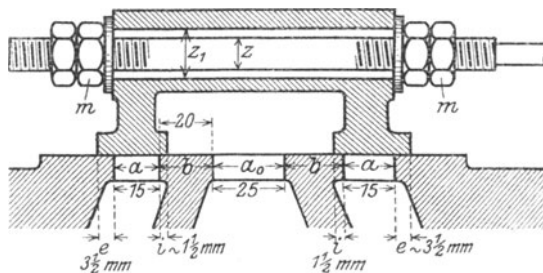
Muschelschieber an einem Zylinder von 190 mm Durchmesser. Diese Figur gilt auch für die Kolbenschieber, nur daß bei diesen wegen der inneren Einförmung (Fig. 34 u. 35) die Überdeckungen e und i vertauscht sind.
